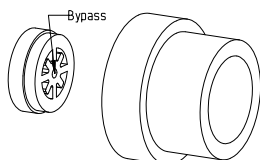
Durchflussbegrenzer im Wasser-Zulauf mit Bypassbohrung
